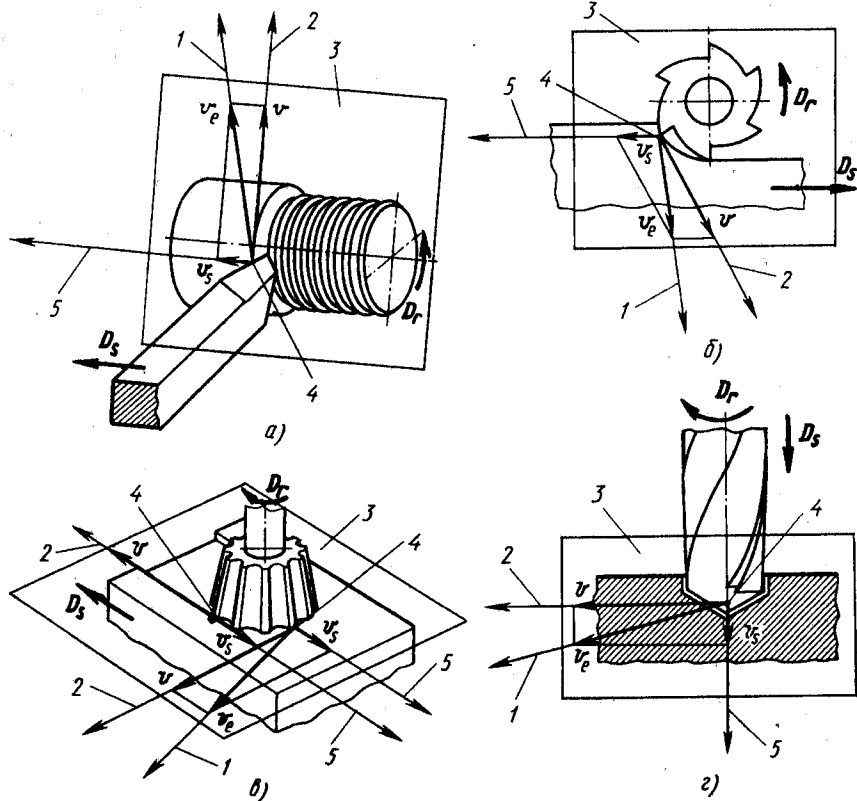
Элементы движений в процессе резания: а — обтачивание, б — периферийное фрезерование, в — фрезерование концевой фрезой, г — сверление; 1 — направление скорости результирующего движения резания, 2 — направление скорости главного движения резания, 3 — рабочая плоскость  $P_S$ , 4 — рассматриваемая точка режущей кромки, 5 — направление скорости движения подачи
